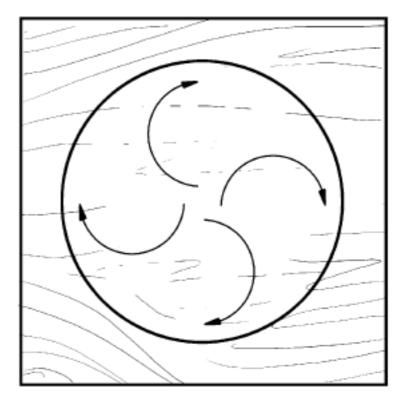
Выполнение круглой вогнутой выемки на торце заготовки вторым способом изогнутыми линиями (стрелками показано направление движения инструмента)
